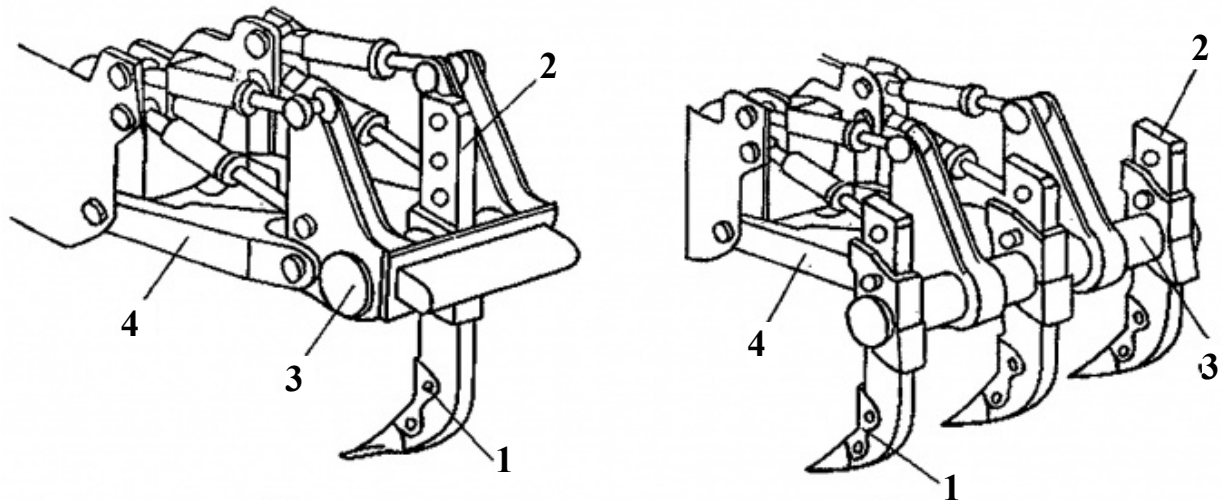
Рами кріплення стійок розпушувача: а – внутрішня; б – охоплювальна;
